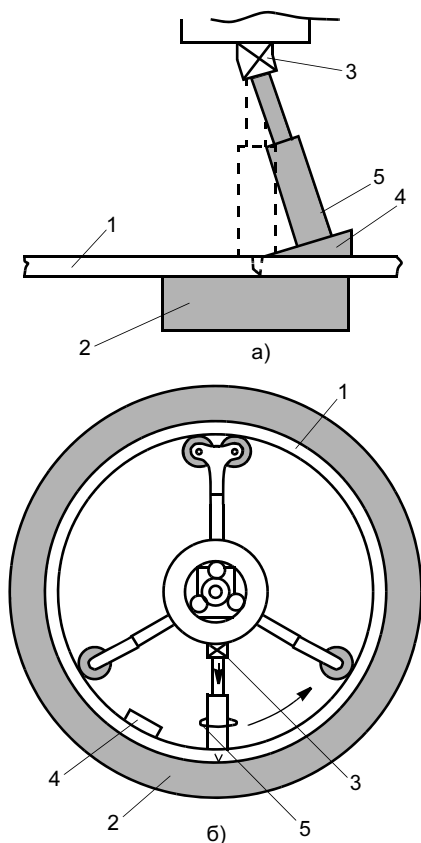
Схема СТП кольцевого соединения трубы: а, б — вид сбоку и вдоль оси трубы; 1 — труба; 2 — опорное кольцо; 3 — шарнирное соединение; 4 — недостающая клиновидная пластина для окончания сварки без кратера; 5 — сварочная головка
